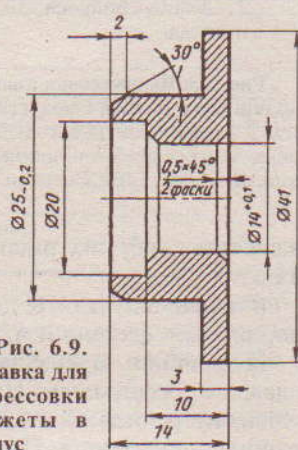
Оправка для запрессовки манжеты в корпус
